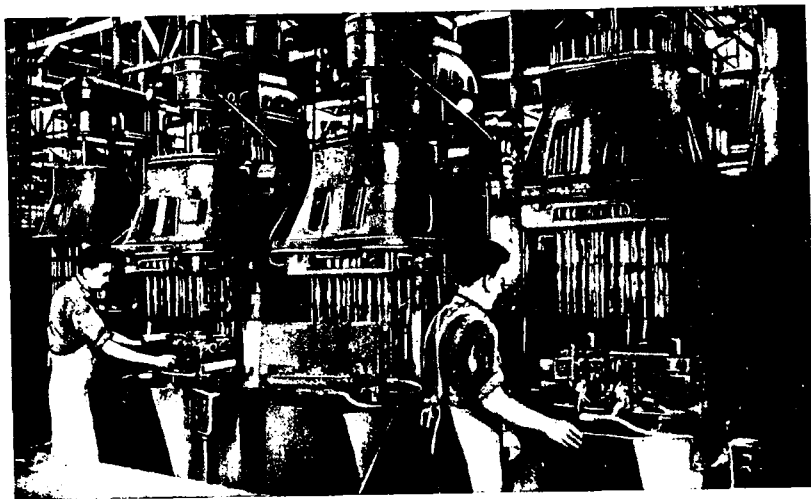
Фрезеровка деталей на токарно-револьверном станке
